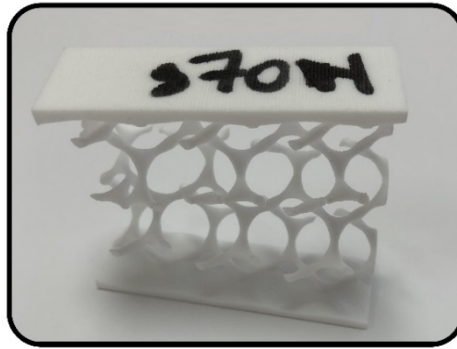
Struttura g70 in seguito all'esecuzione della prova statica [2]
